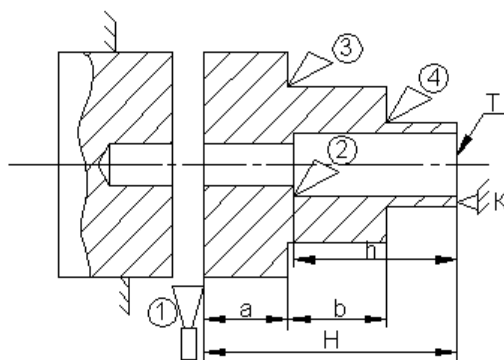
Схема обработки на токарно-револьверном станке.
